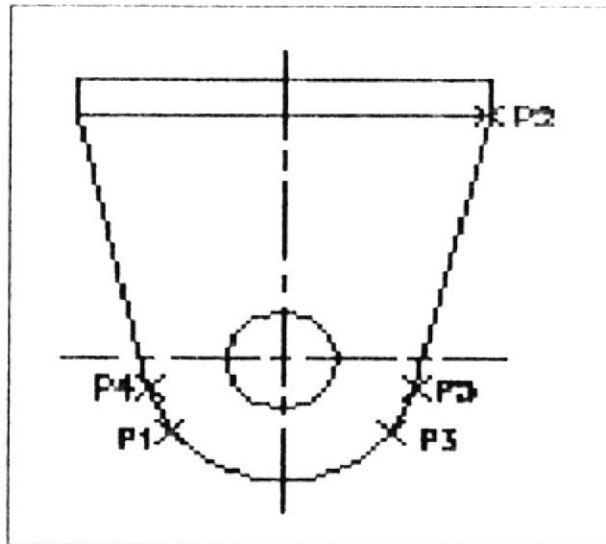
PUNTOS DE REFERENCIA 1 (DIBUJO DE DESPIECE)
